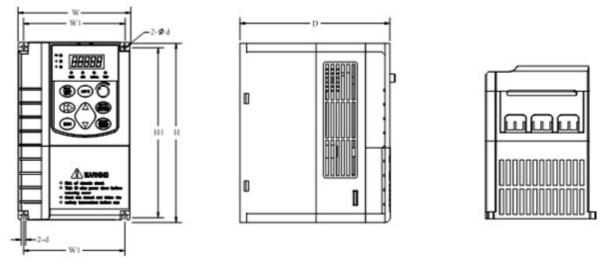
Внешний вид инвертора SL9 в пластиковом корпусе
